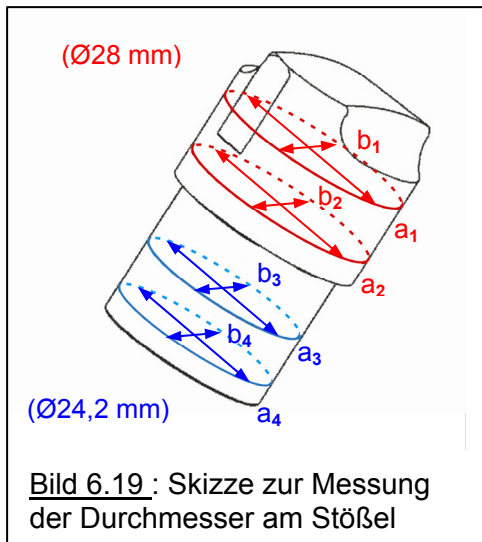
Skizze zur Messung der Durchmesser am Stößel
